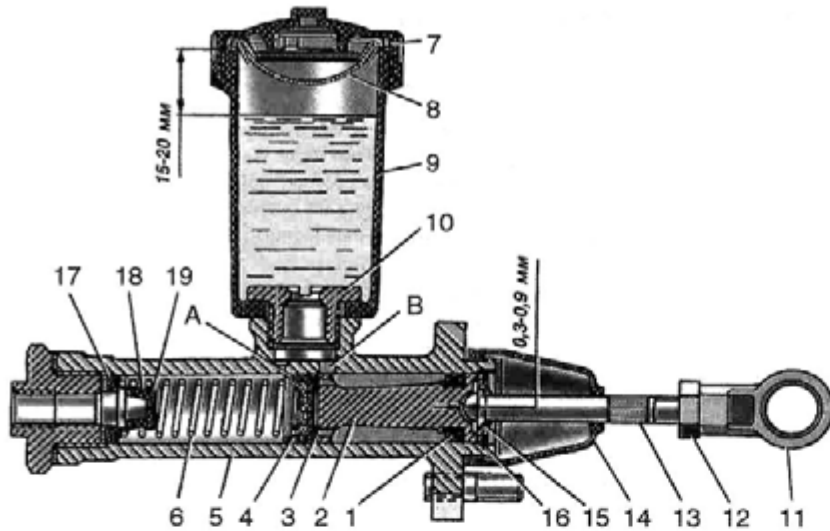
Главный цилиндр привода выключения сцепления:
